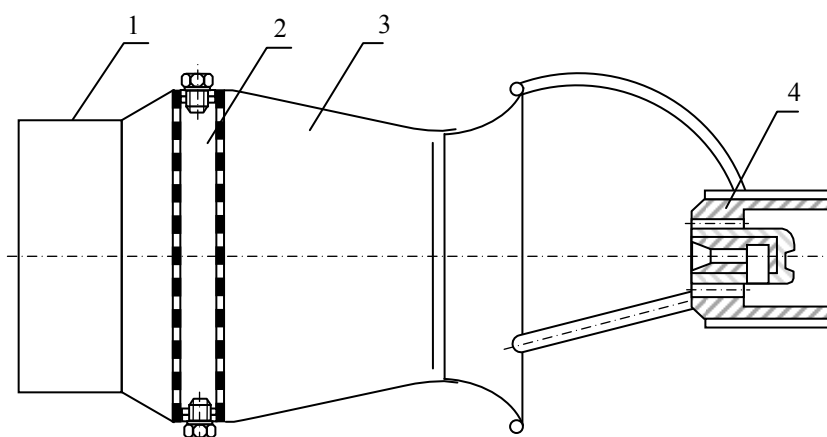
Генератор повітряно-механічної піни середньої кратності для стаціонарної установки типу ГПСС: 1– направляюча частина для потоку піни; 2– пакет сіток; 3– корпус; 4– відцентровий розпилювач
